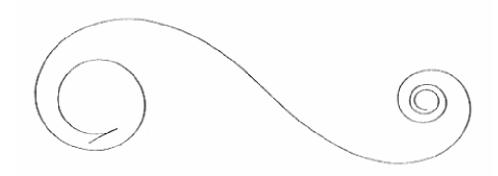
Muelle real en su posición de desenrollado fuera del barrilete
